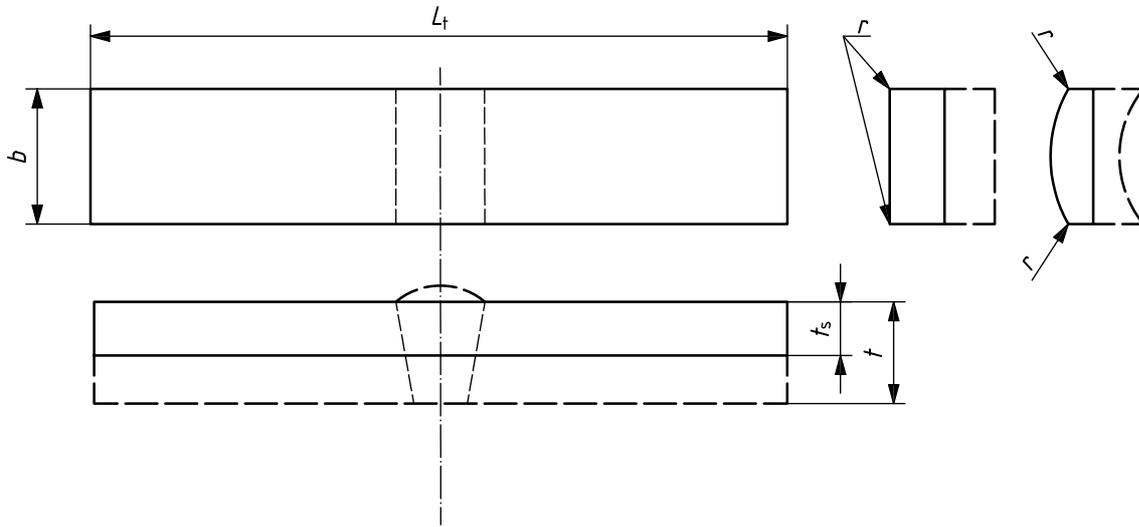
Éprouvette de pliage transversal endroit sur soudure bout à bout (TFBB)
